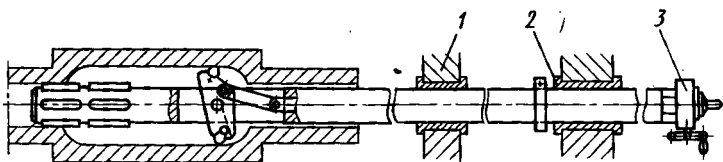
Схема работы борштанги для сверления в валах отверстий бутылочной формы:
